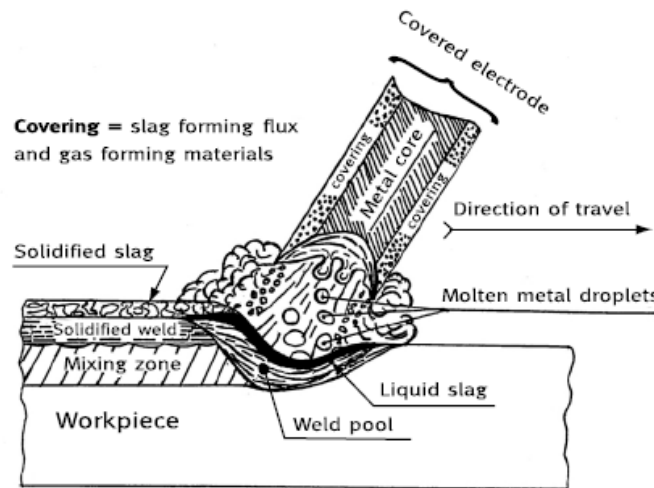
Schéma du soudage à l'électrode enrobée [9]
